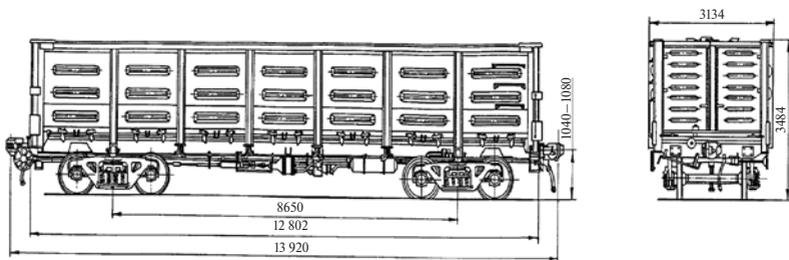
Четырехосный цельнометаллический полувагон с торцевыми двухстворчатыми дверями модели 12-753
